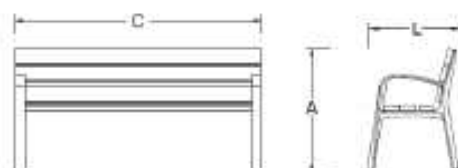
Croquis del Banco Coimbra. (Fuente: <http://www.bricantel.pt/es/>)
